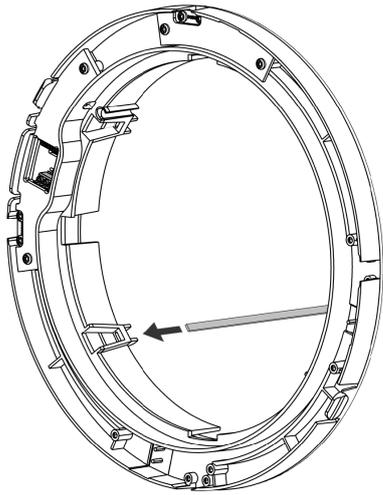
Insérez les bandes du chapeau de ventilation dans le chapeau de façade intérieur.
